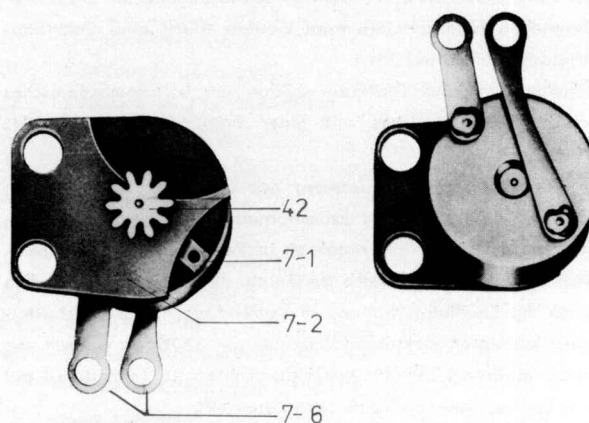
Motor U. (Schrittmotor) in zwei Ansichten Ausf. I
